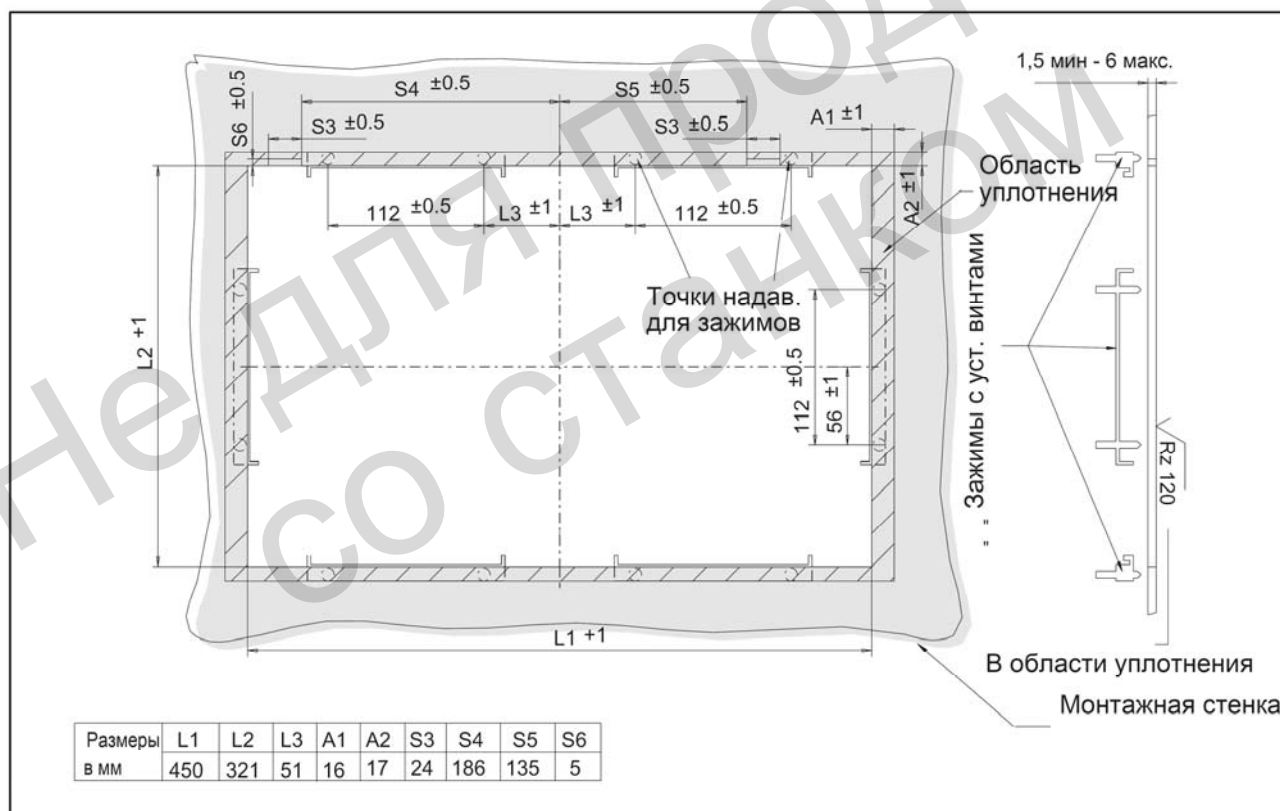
Габаритный чертеж для монтажа панели оператора OP 015A
